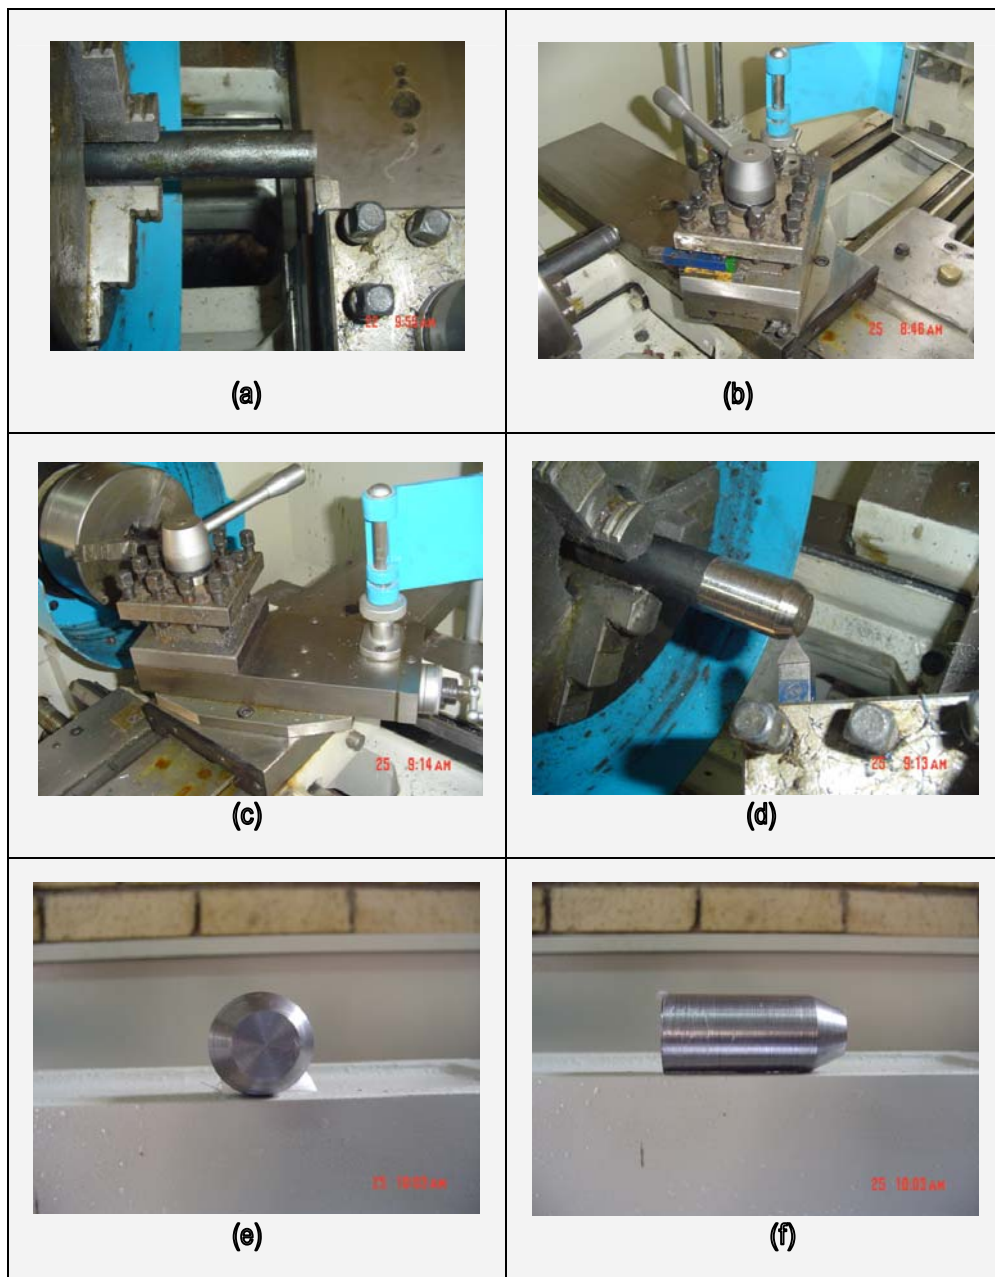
Conicidad. (a) cilindrar, (b) ajuste del carro superior, (c) acercamiento del carro longitudinal, (d) formación del cono, (e) vista frontal, (f) vista lateral.
